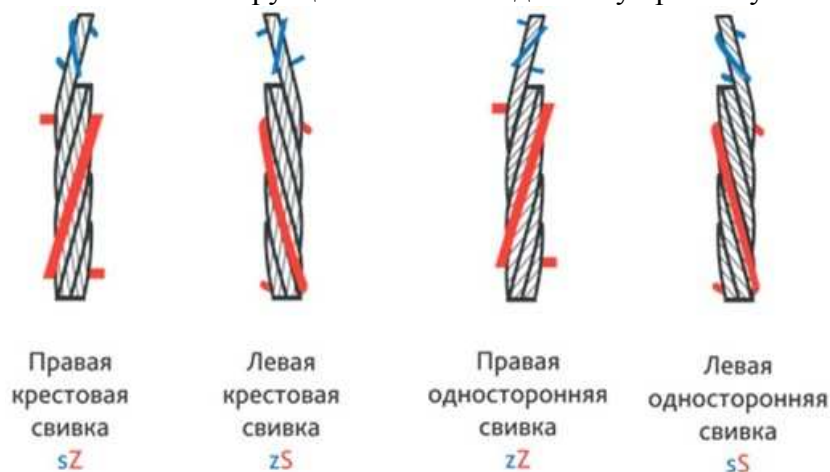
Отличия конструкций канатов по направлению и типу свивки
